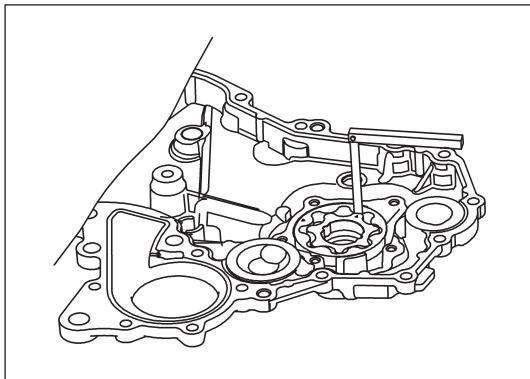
Проверка зазора в зацеплении между ведущей и ведомой шестернями
